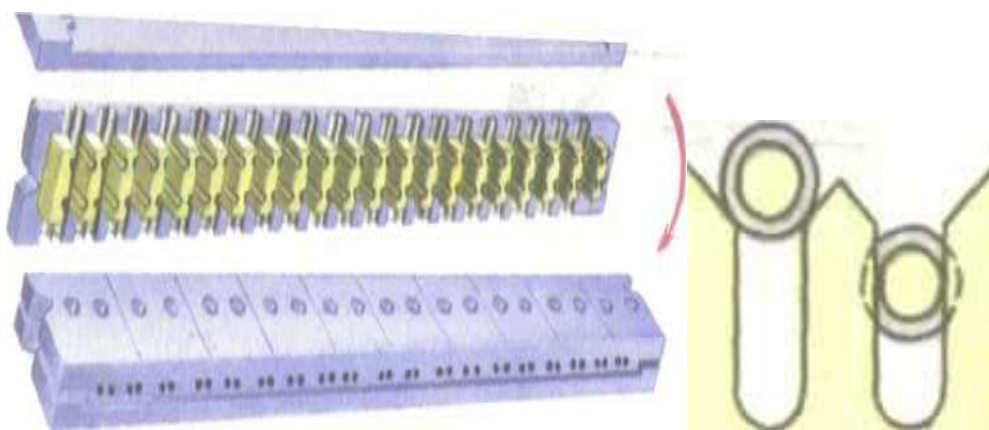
Десятипарный соединитель для кабелей ГТС
